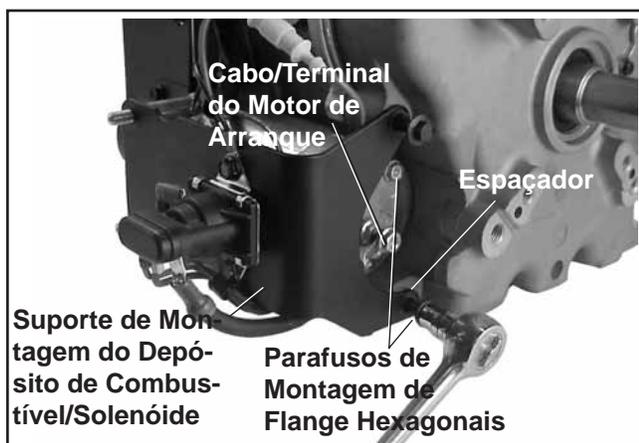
Retirar o Accionamento do Motor de Arranque Bendix.
